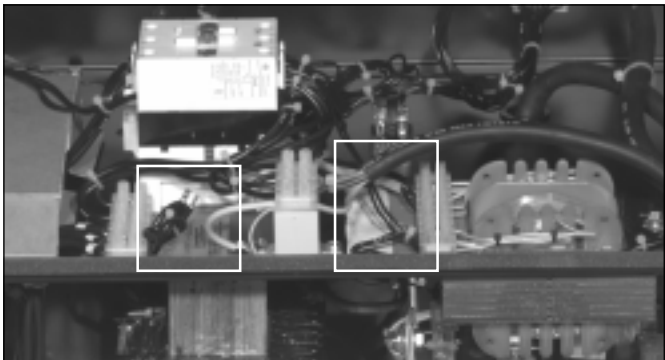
Klemmbrett für Schweiß- und Steuertrafo
